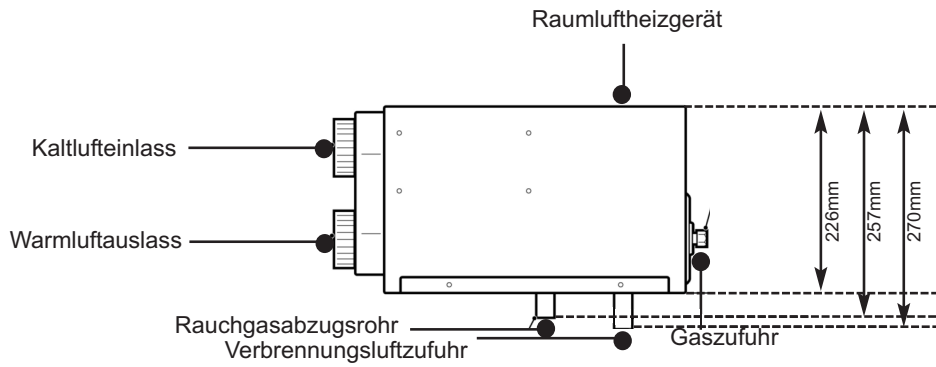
Interne Montage - Seitenansicht - SH2202 oder SC2202
